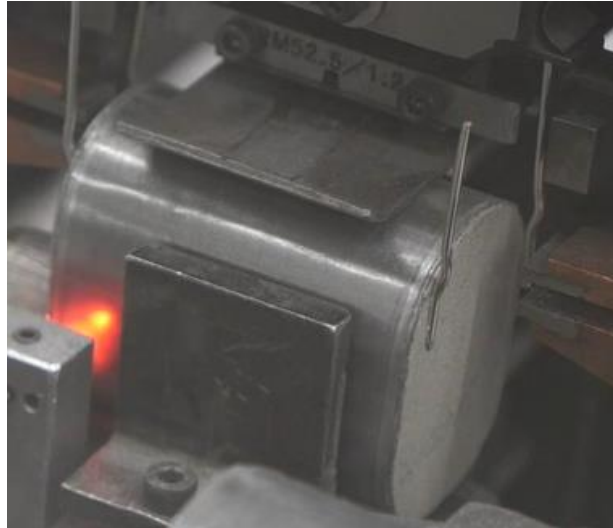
Soldadura de uma bobina com 4 arames, numa máquina de montagem automática
